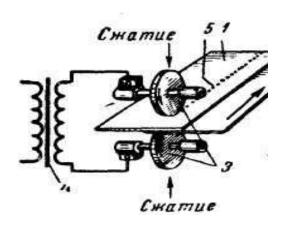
Схема процесса шовной сварки
